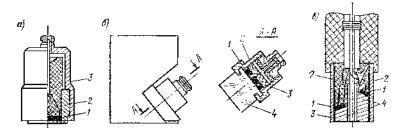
Конструкции искателей a= прямого; b= паклонного; b= раздельно-совмещенного; b= пьезоэлемент; b= деэлфер; b= корпус; b= призма
